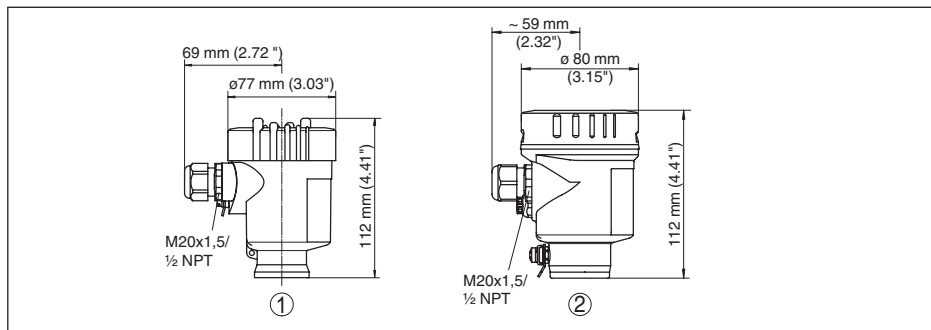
Корпус электроники (с установленным модулем индикации и настройки крышка корпуса выше на 9 мм)
